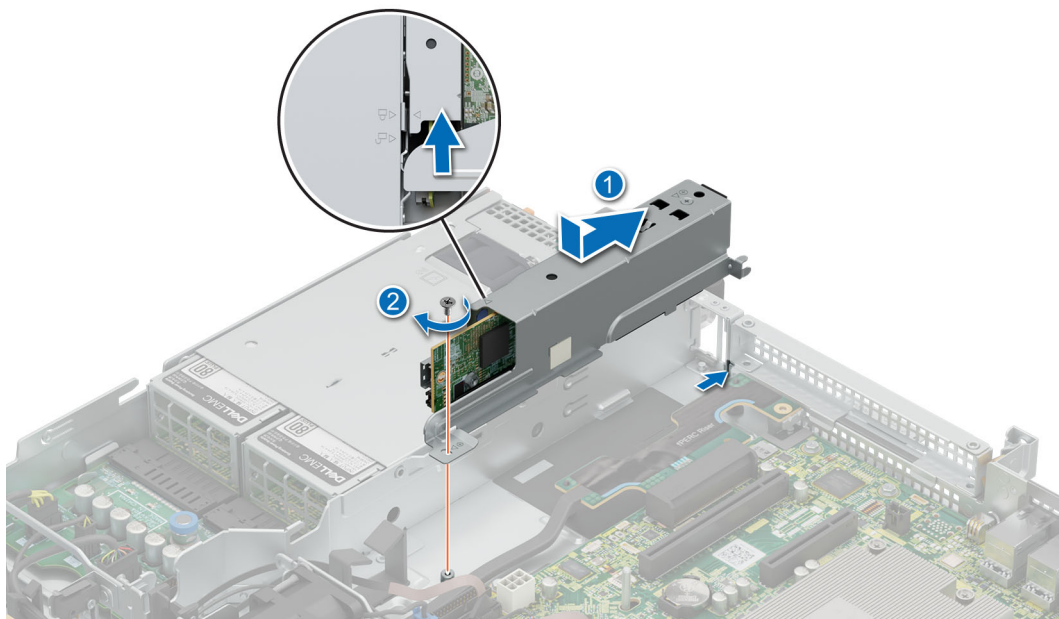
Installieren des BOSS-N1-Gehäuses
